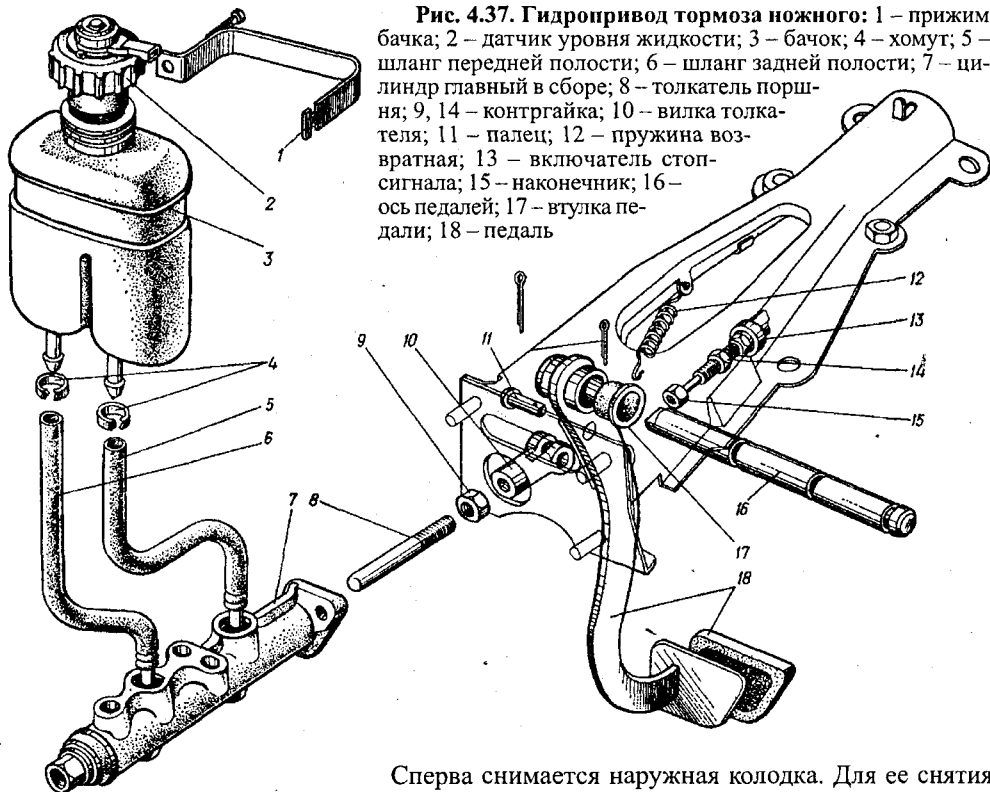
Гидропривод тормоза ножного: 1 — прижим бабка; 2 — датчик уровня жидкости; 3 — бачок; 4 — хомут; 5 — шланг передней полости; 6 — шланг задней полости; 7 — цилиндр главный в сборе; 8 — толкатель поршня; 9, 14 — контргайка; 10 — вилка толкателя; 11 — палец; 12 — пружина возвратная; 13 — включатель стоп-сигнала; 15 — наконечник; 16 — ось педалей; 17 — втулка педалей; 18 — педаль
